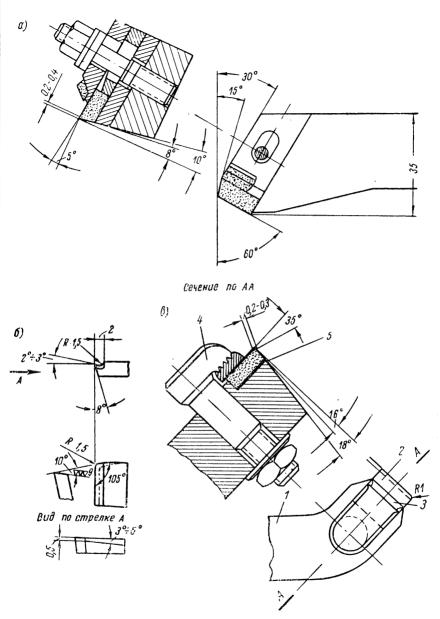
Проходной резец для получистового обтачивания заготовок жестких валов.
